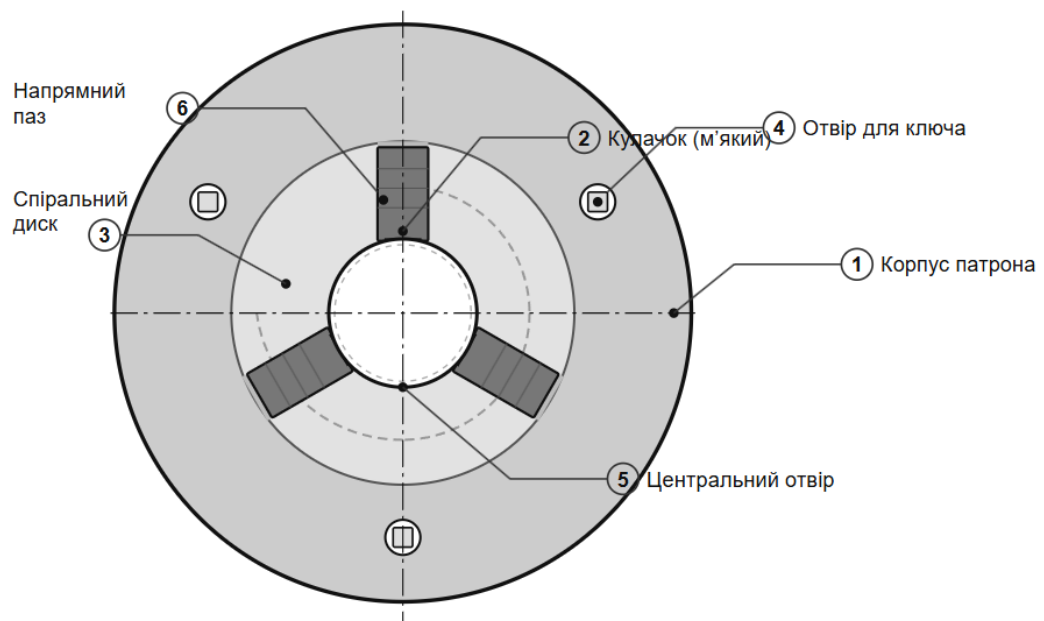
Трикулачковий самоцентруючий патрон (вигляд з торця)
